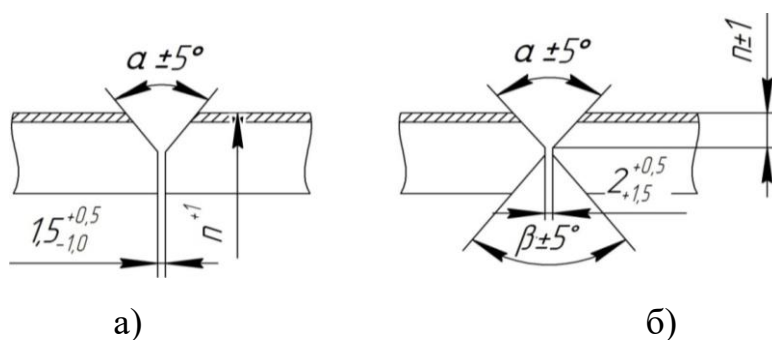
Разделка кромок двухслойных листов толщиной до 20 мм при комбинированном способе сварки:
